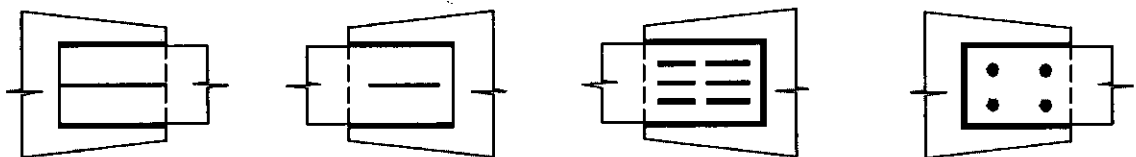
Soldaduras Tipo Tarugo o Ranura
